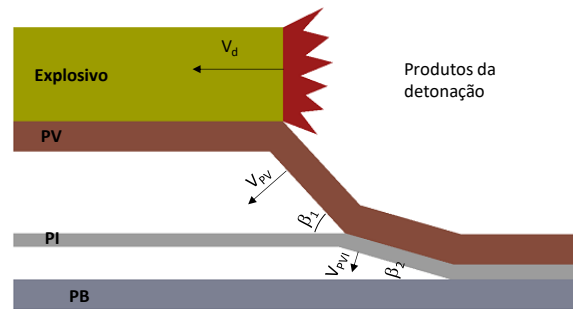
Representação esquemática do processo de soldadura por explosão, com placa intermédia, em configuração plana paralela.
